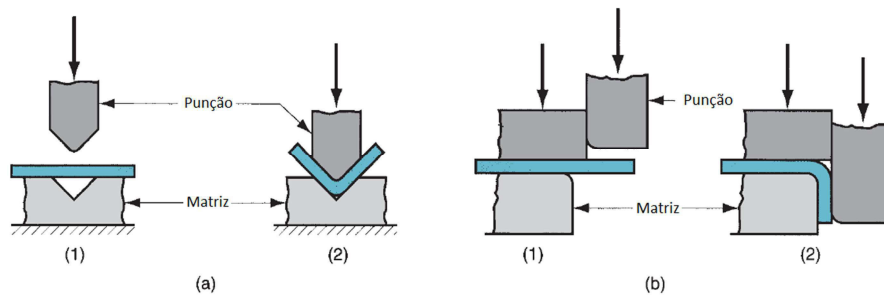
Métodos de quinagem de uma chapa: (a) quinagem em V e (b) quinagem de canto; (1) antes e (2) depois da quinagem [FONTE: adaptado [58]].
